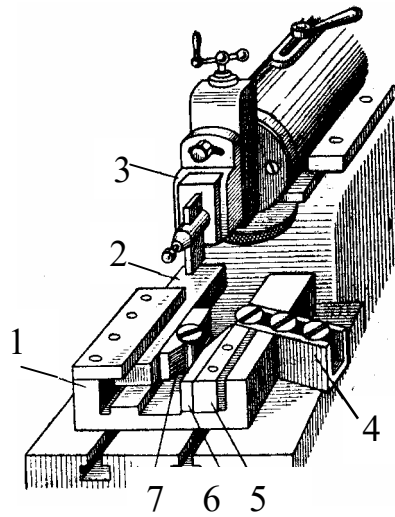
Пристосування для накатування різьби на поперечно-стругальному верстаті: 1 – корпус; 2 – повзун; 3 – різцетримач; 4 – магазин; 5 - плашкодержимач; 6, 7 - плашки
